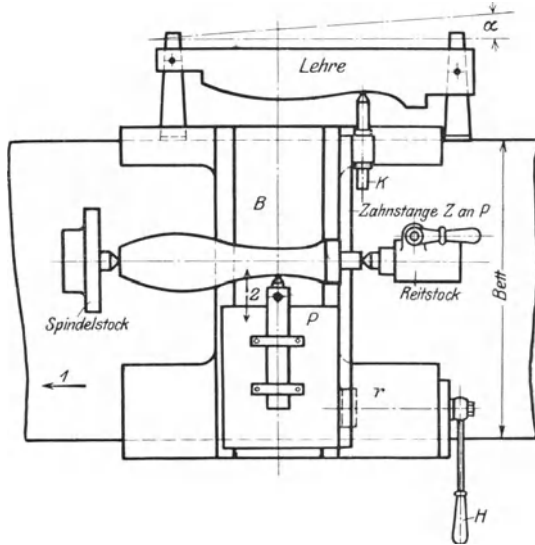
Werkzeugschlitten einer Formdrehbank.
